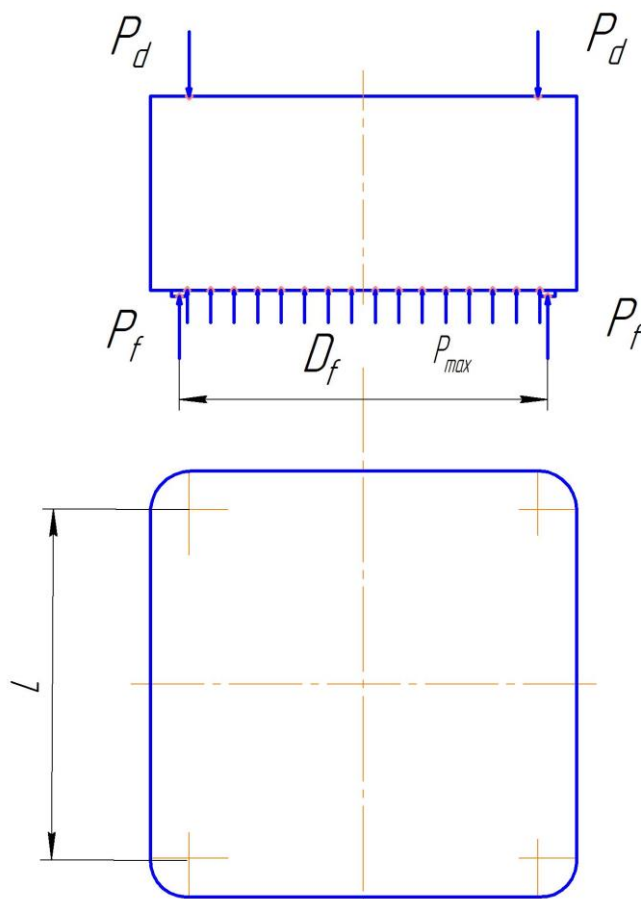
Розрахункова схема кришки робочого циліндру
